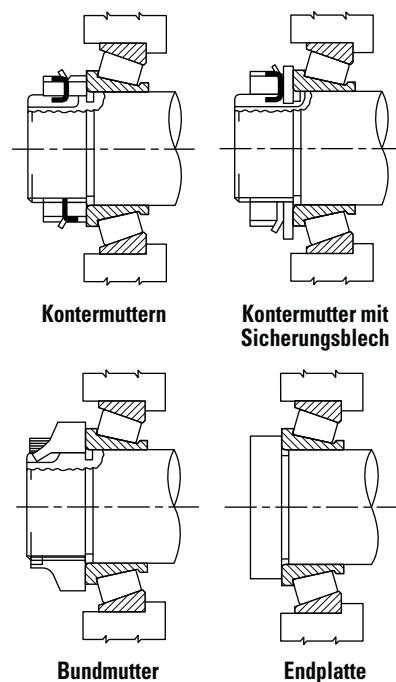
Vorrichtungen zur Lagereinstellung - indirekte Montage.
